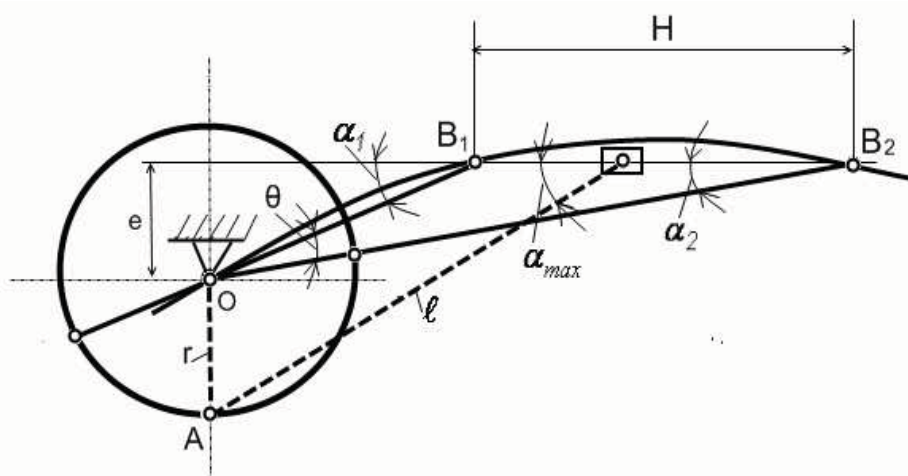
Кинематическая схема кривошипно - шатунного привода клетки станков ХПТ
